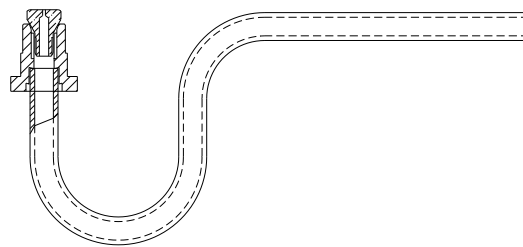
TUBERIA DE ALUMINIO CON INYECTOR INCORPORADO
